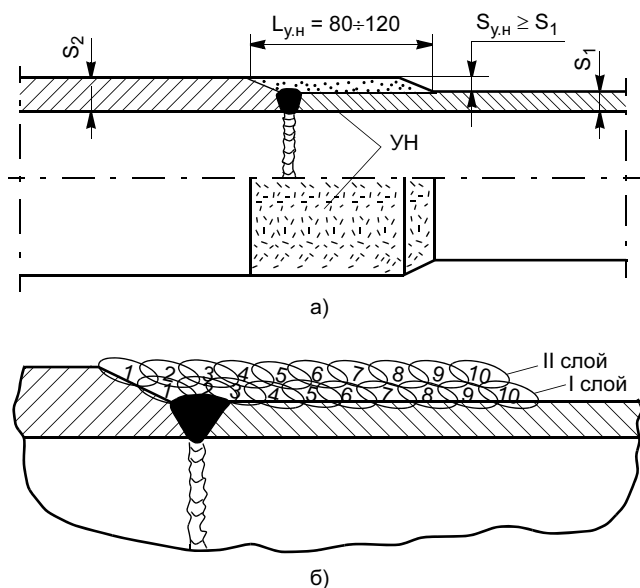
Укрепление поврежденного ССС_{ртз} нанесением усиливающей (кольцевой) наплавки: а — общий вид и размер усиливающей наплавки; б — очередность нанесения кольцевых валиков каждого слоя
